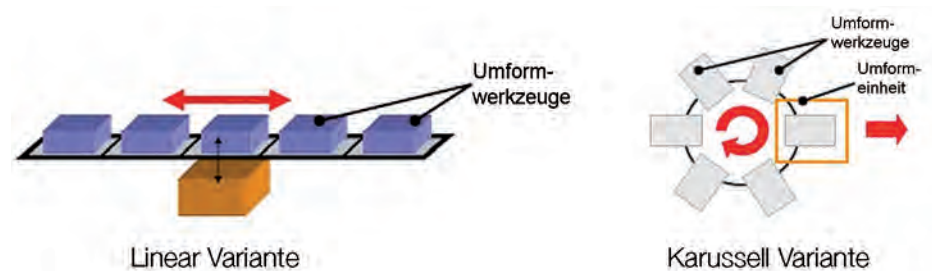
Einpunktpresse mit versetzbaren Werkzeugen.
